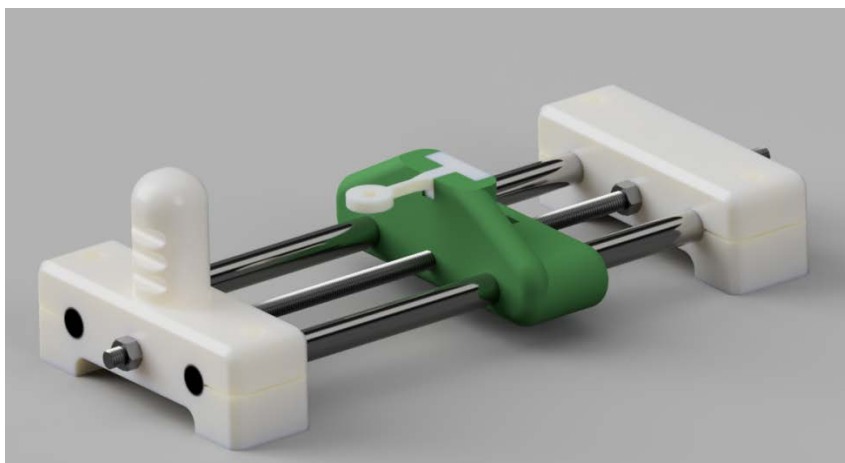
Фотореалистичный вид станда до оптимизации
